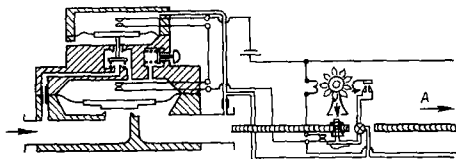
Схема АРК для бытовой газовой плиты.
